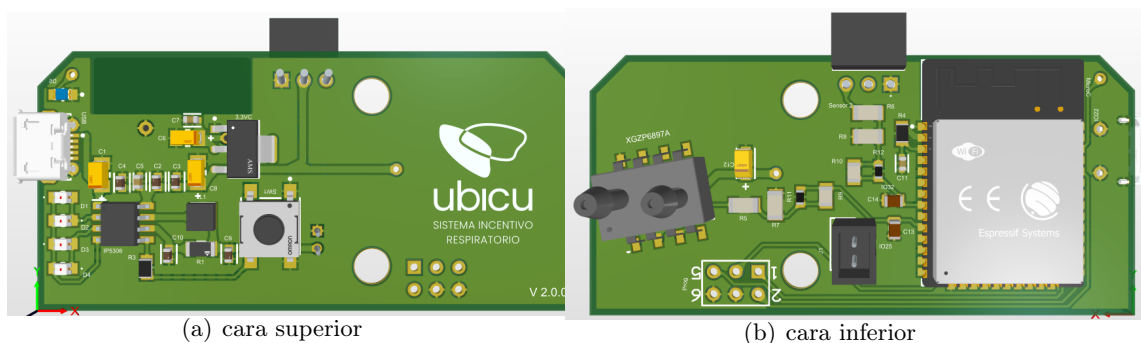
CAD PCB Ubicu analógico del dispositivo final Ubicu.
